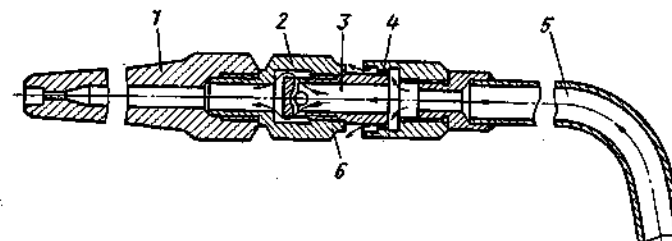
Наконечник с подогревателем для сварки на пропан-бутане:
